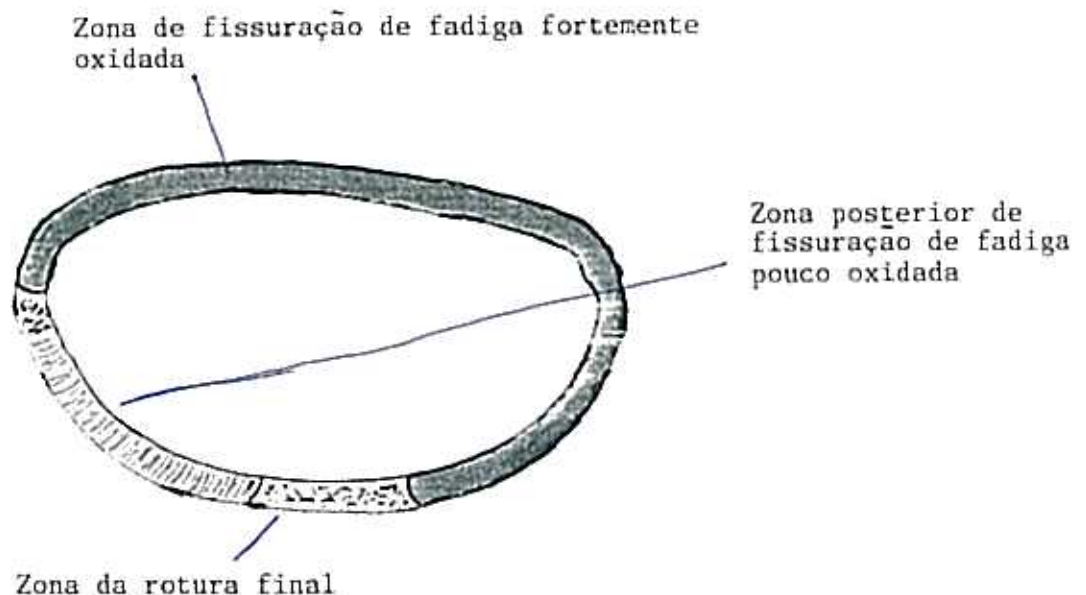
Representação esquemática da superfície fracturada 1-2 da Fig.1
